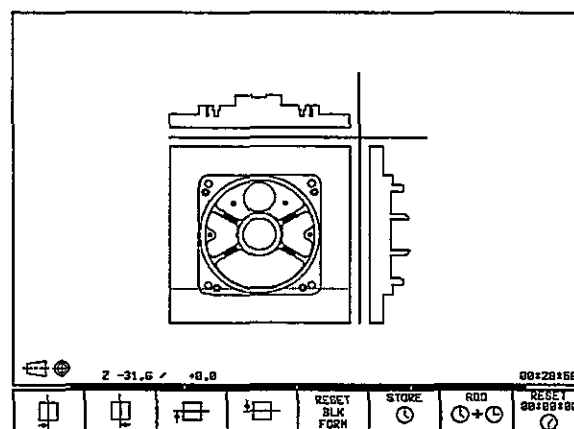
Plans avec vue en coupe pour la représentation en 3 plans
